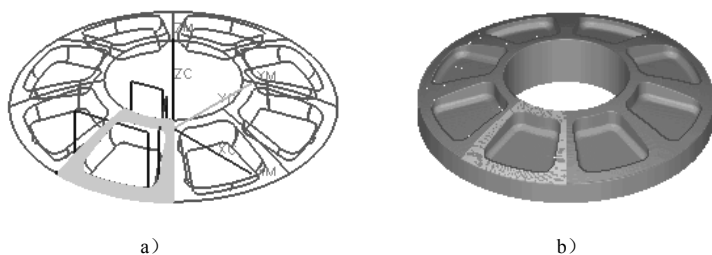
固定轴曲面轮廓铣精加工的“切削刀具路径”和“切削验证”
